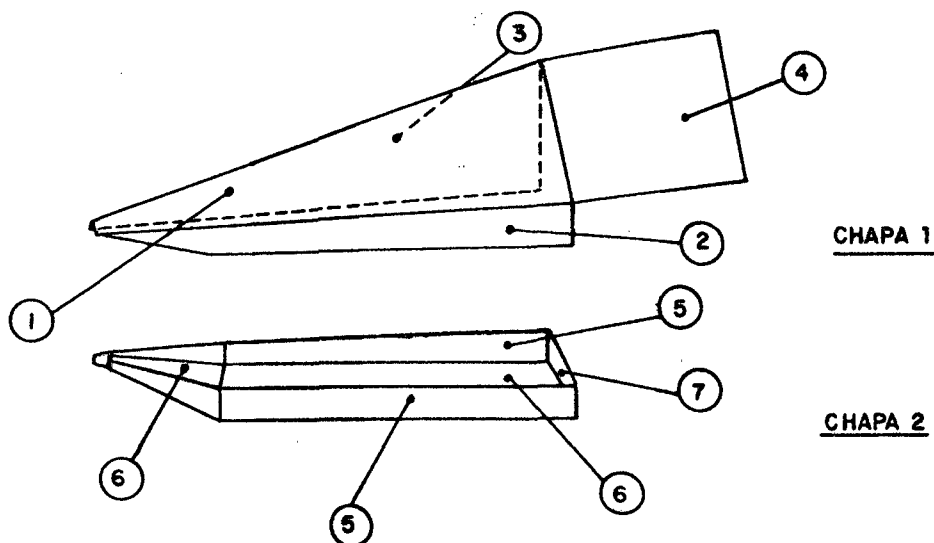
Chapas metálicas que constituem o levantador.
